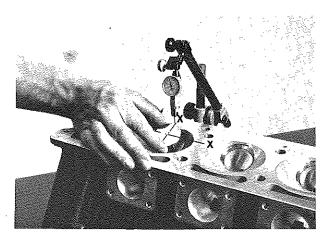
Misurare il gioco valvola-guida valvola Measuring the clearance between valve guide and valve
